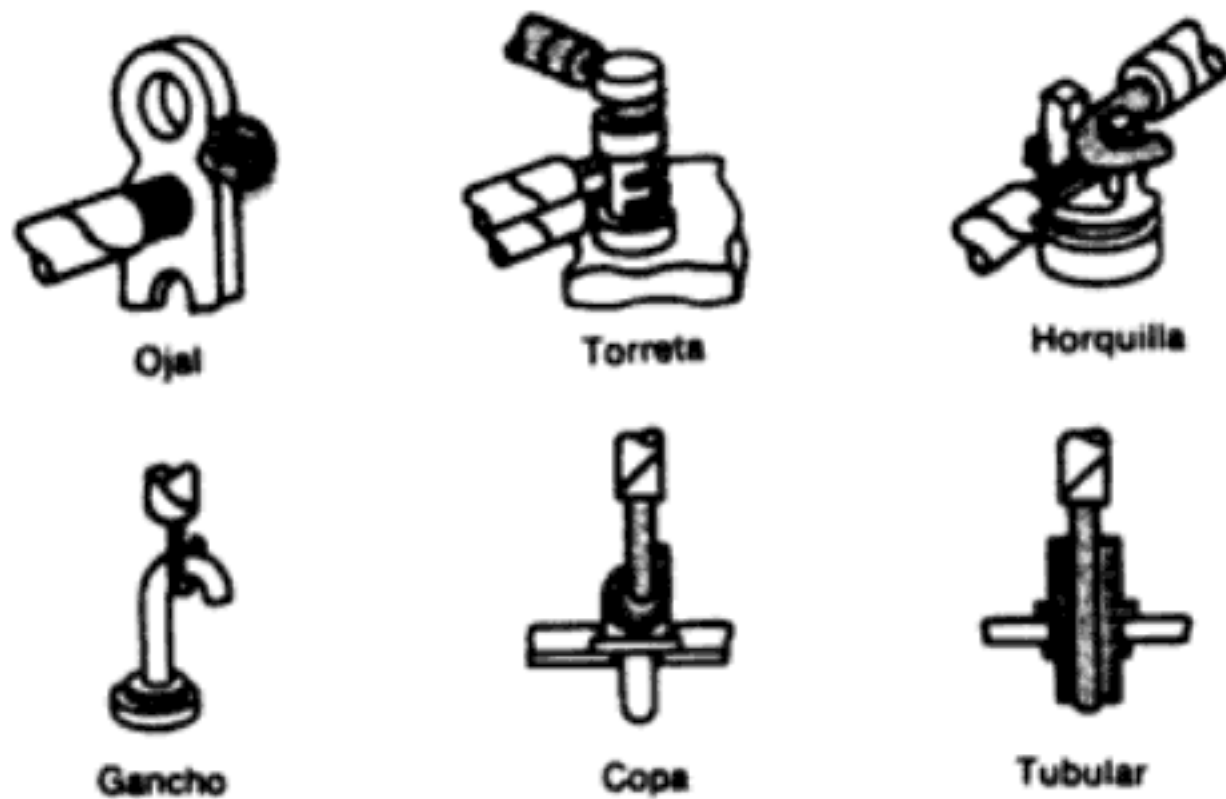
Fijación del conductor al borne antes de soldar.
